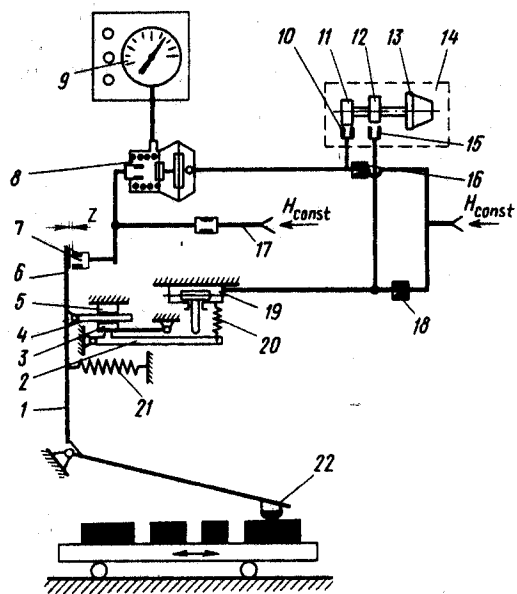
Схема измерительного устройства для контроля заготовок на плоскошлифовальном станке
